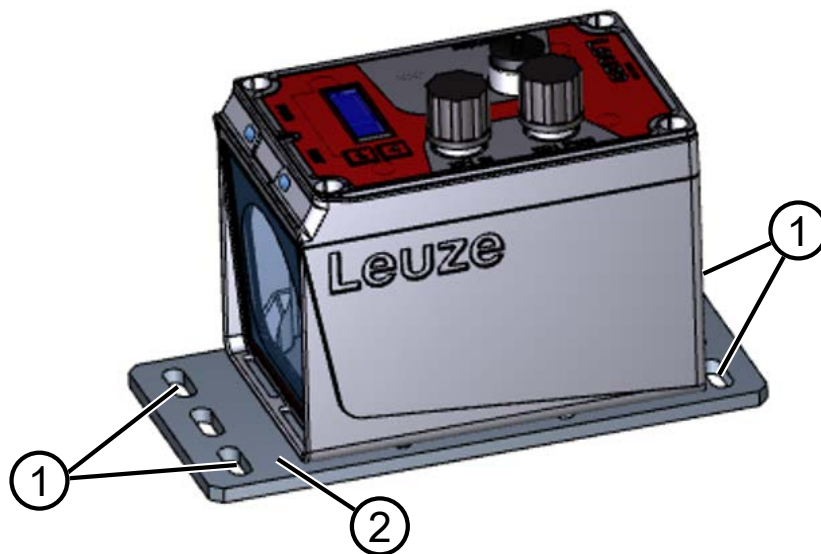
Ejemplo de montaje con placa adaptadora (BT)
